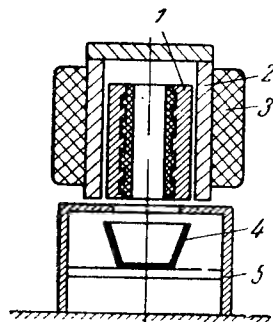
Индукционный нагреватель для выплавки баббита.
